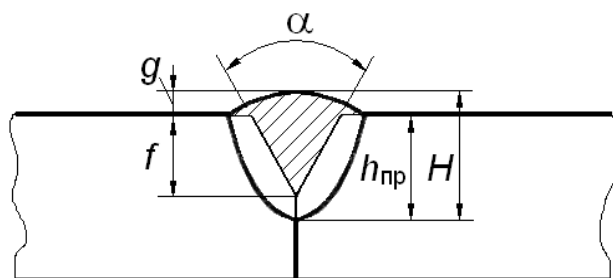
Сечение шва при сварке стыкового соединения с разделкой кромок
